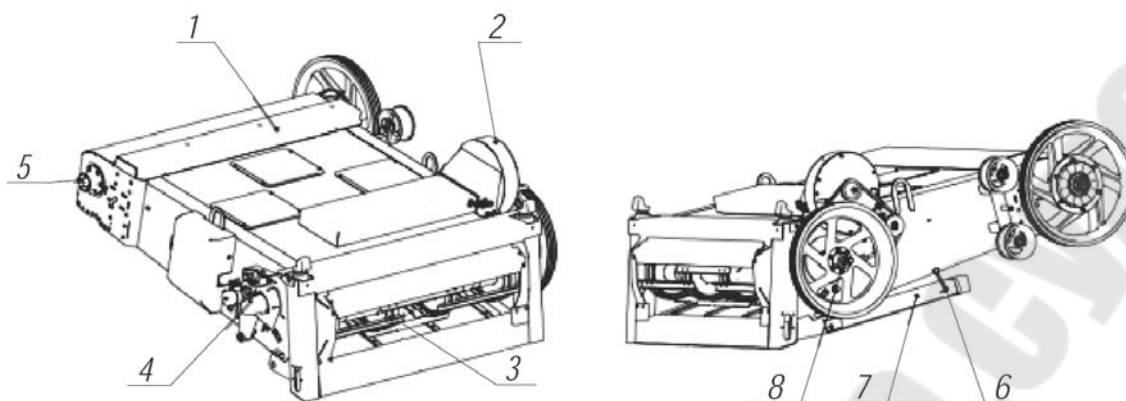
Конструктивная схема наклонной камеры: а – вид сверху; б – вид сбоку; 1 – рама; 2 – вентилятор; 3 – транспортер цепочно-планчатый; 4 – механизм реверса; 5 – вал верхний; 6 – цепочка; 7 – упор; 8 – вал
